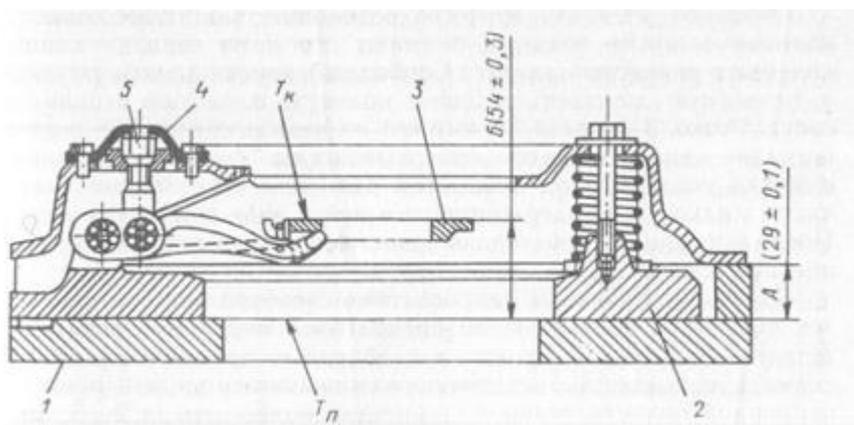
Регулировка положения упорного кольца рычагов выключения сцепления:
